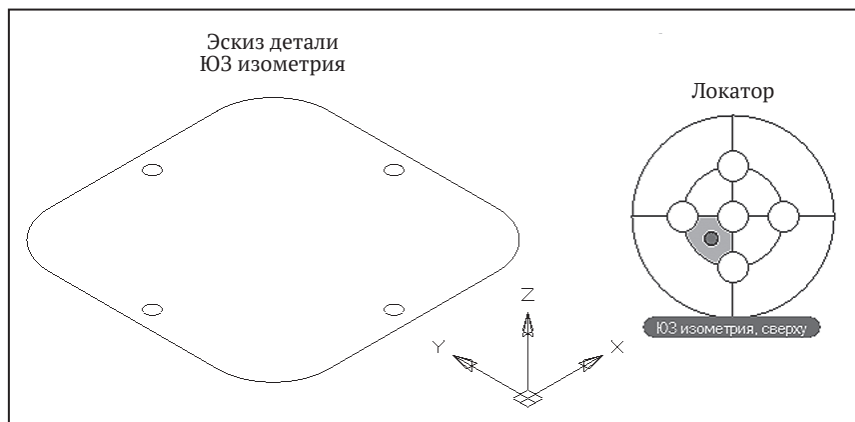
Эскиз вида сверху детали «Колпачок» в ЮЗ изометрии
